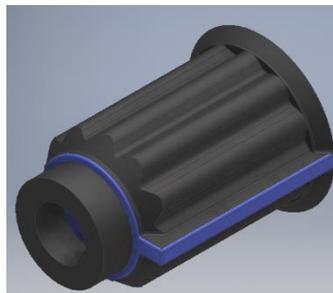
Design da peça de acoplamento do dimmer no motor de passo.
